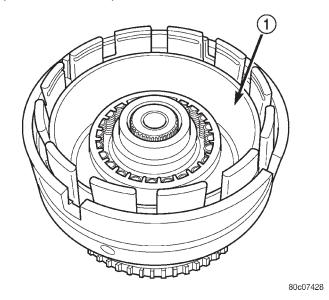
Instalación del émbolo regulador con la herramienta 8252
